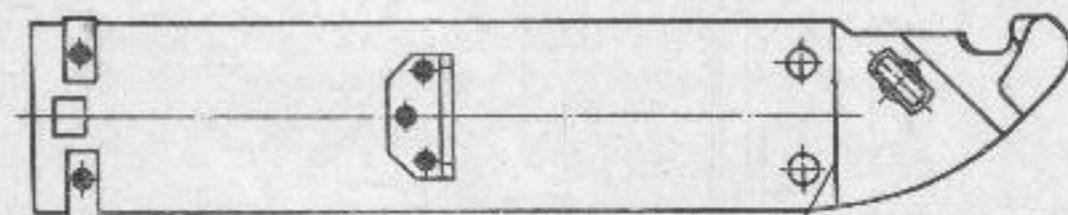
Устранение качки резака в соединении с корпусом ножны:
